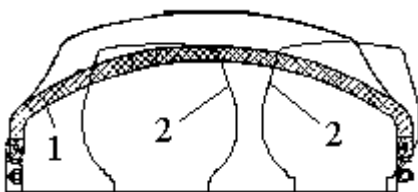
Розріз арочної шини (1) розміру 1140x700, змонтованої на ободі, в порівнянні з профілем шин розміру 260-20 (2)
